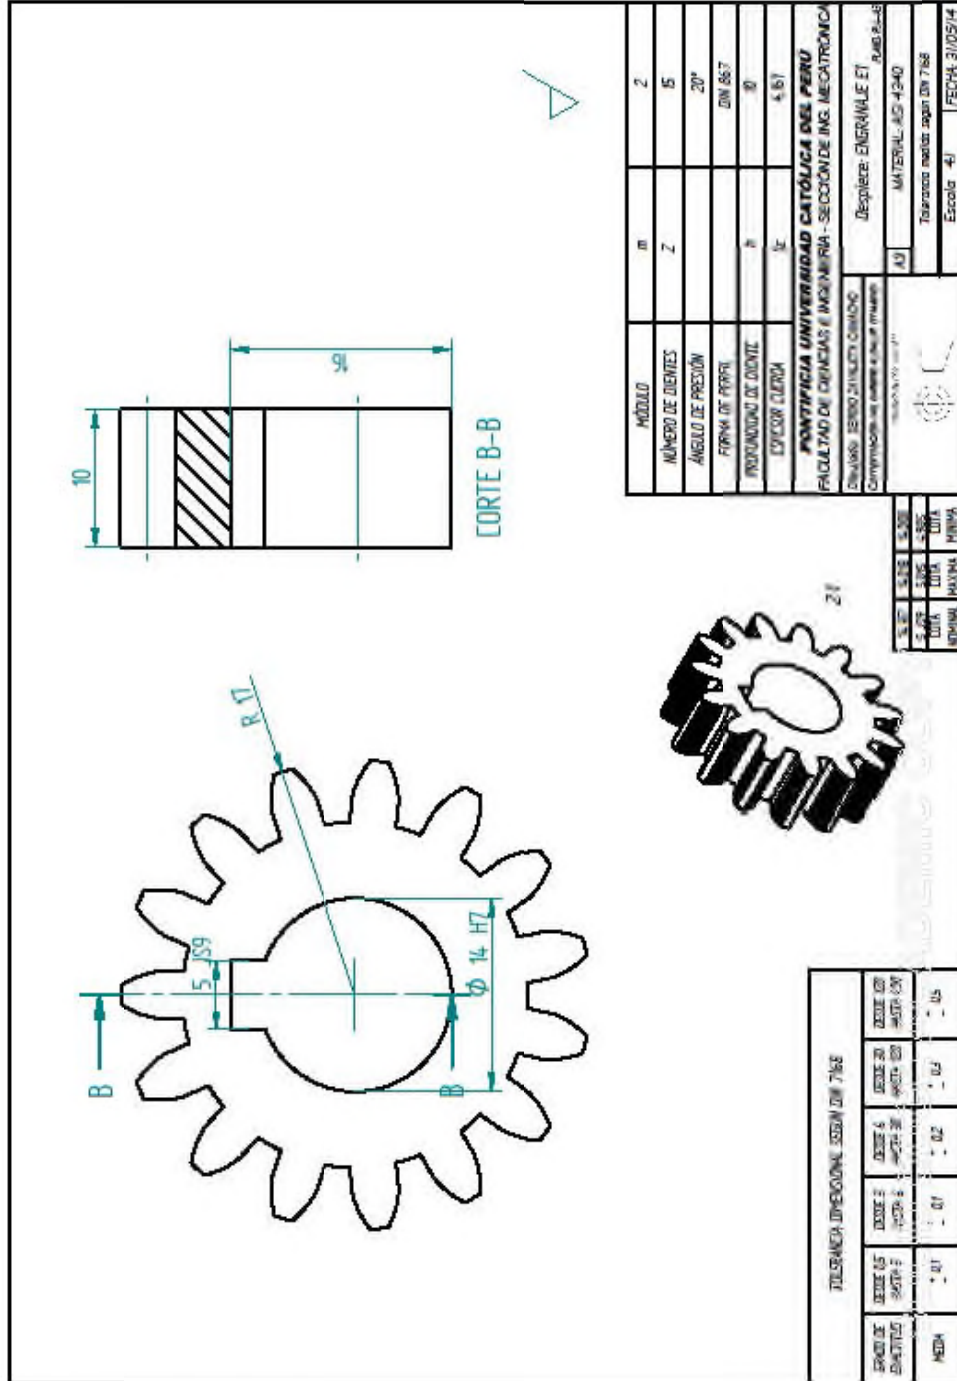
Plano de despiece del engranaje E1. Fuente: Elaboración propia
